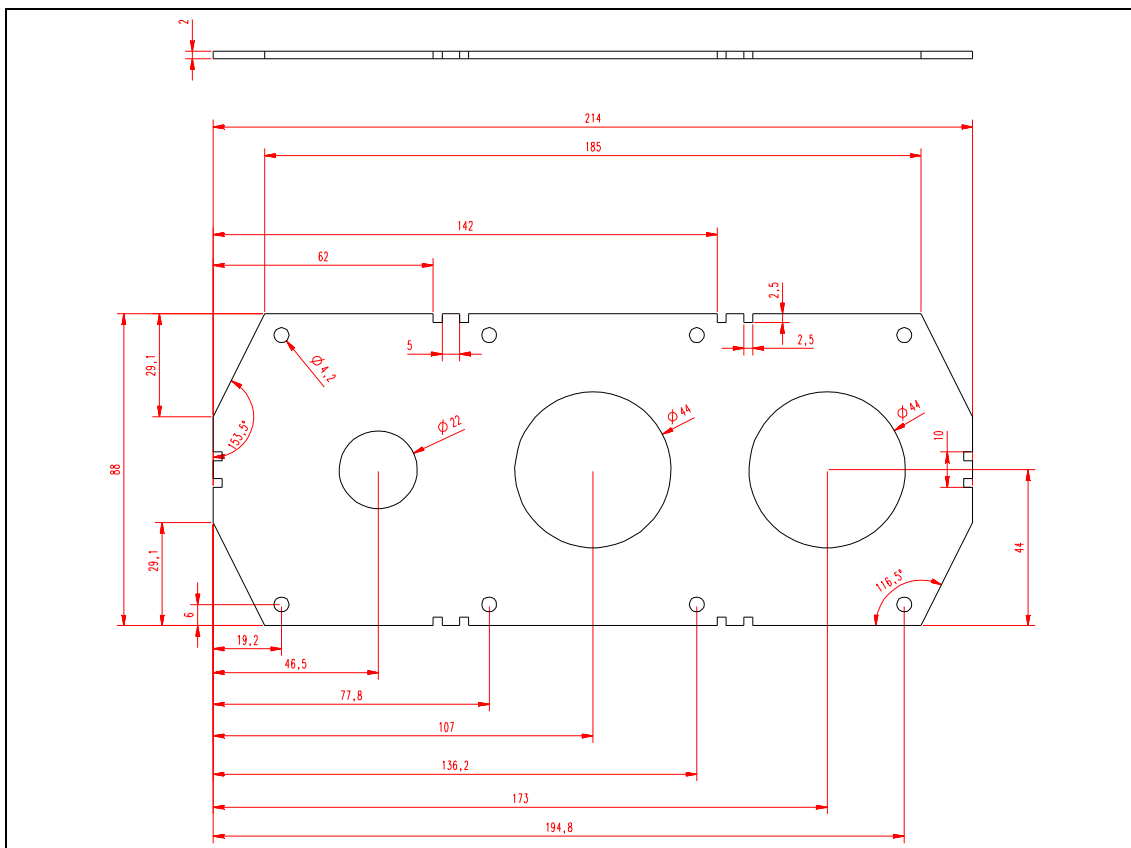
Placca ingresso cavi, MM6 installazioni UL.
